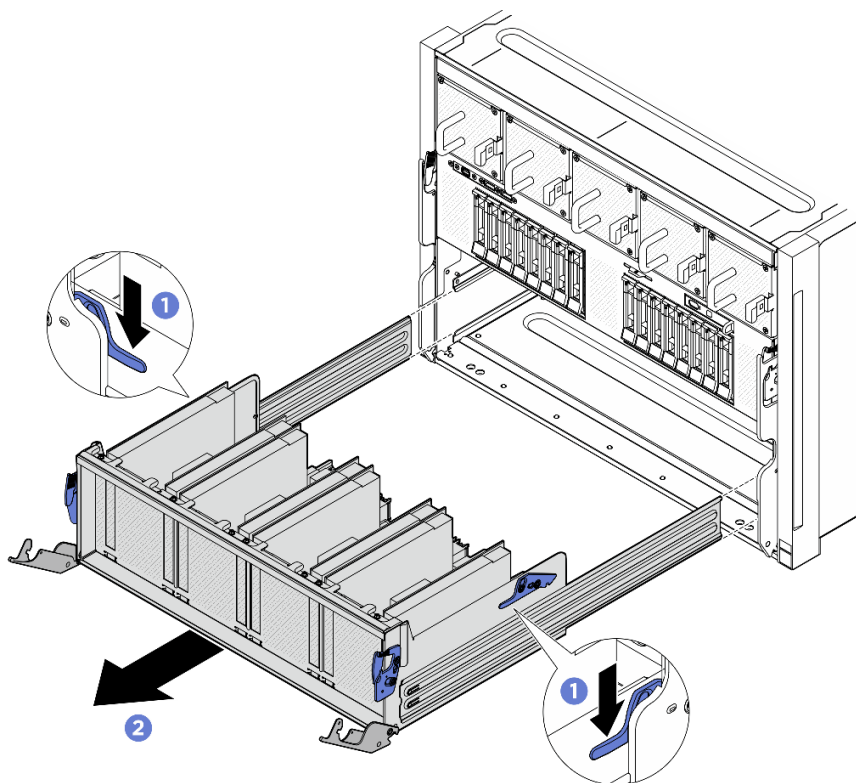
Alternador do comutador PCIe remoção do Alternador de GPU 8U
